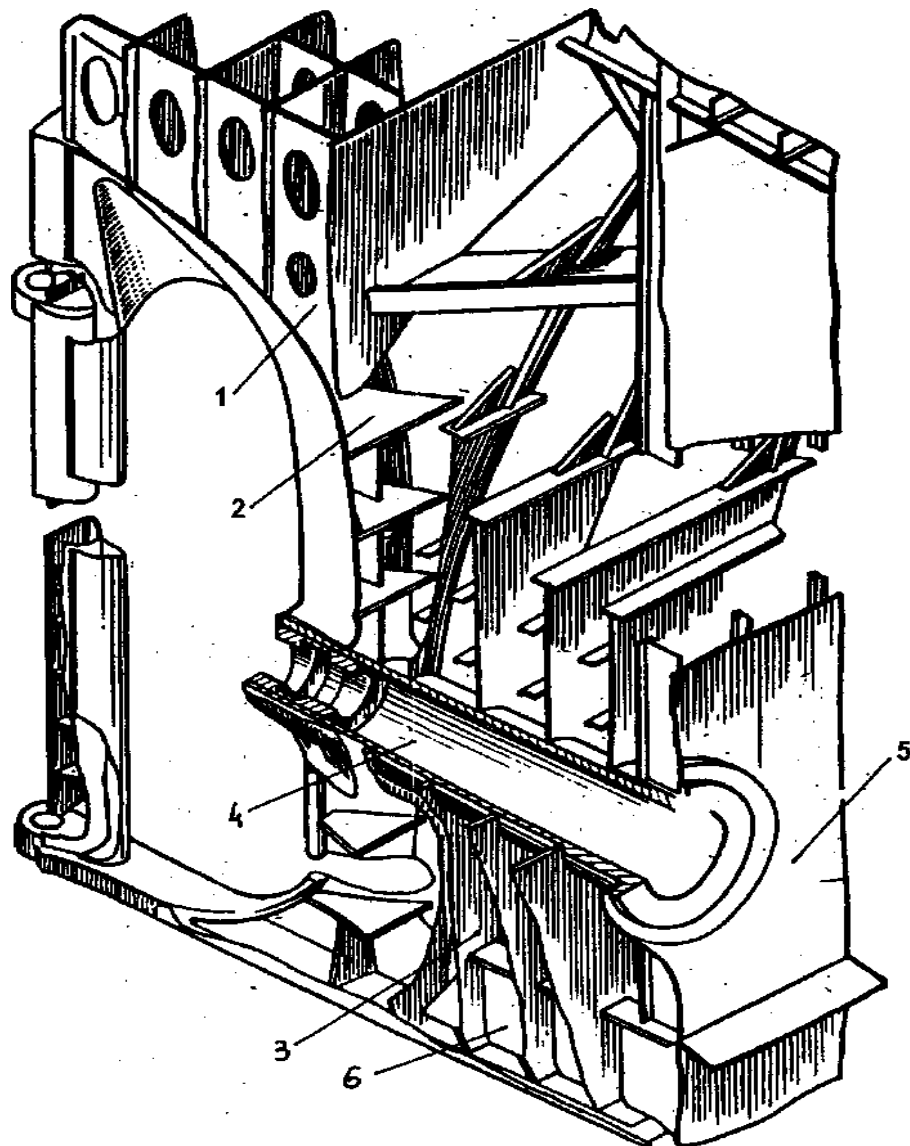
Внутренние конструкции крепления ахтерштевня:
